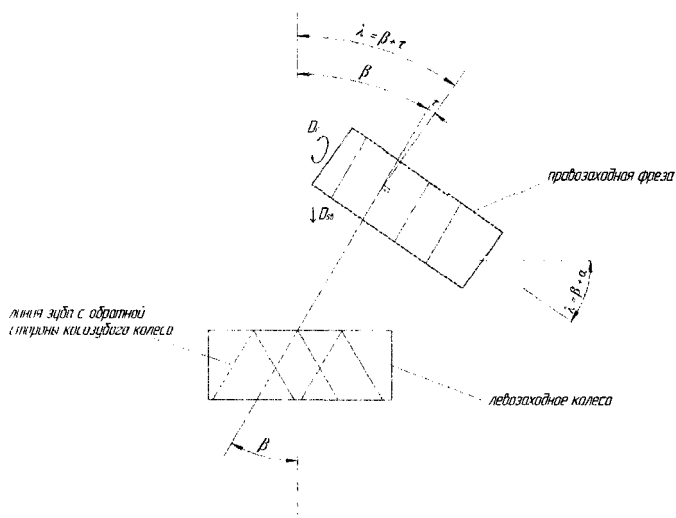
Схема определения угла наклона оси правозаходной червячной фрезы  $\lambda$  относительно горизонтального стола зубофрезерного станка при нарезке левозаходного косозубого колеса с углом наклона зубьев  $\beta$
